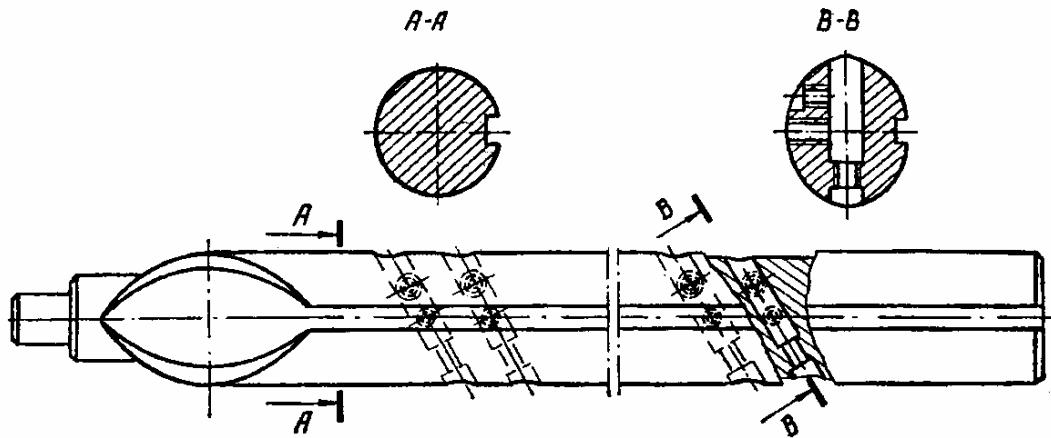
Борштанга для розточування гнізд корінних підшипників блока циліндрів
